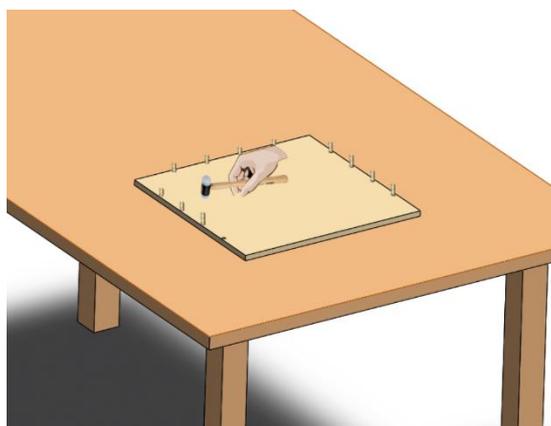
Paso 6 del ensamblaje del cajón (conjunto 2)
